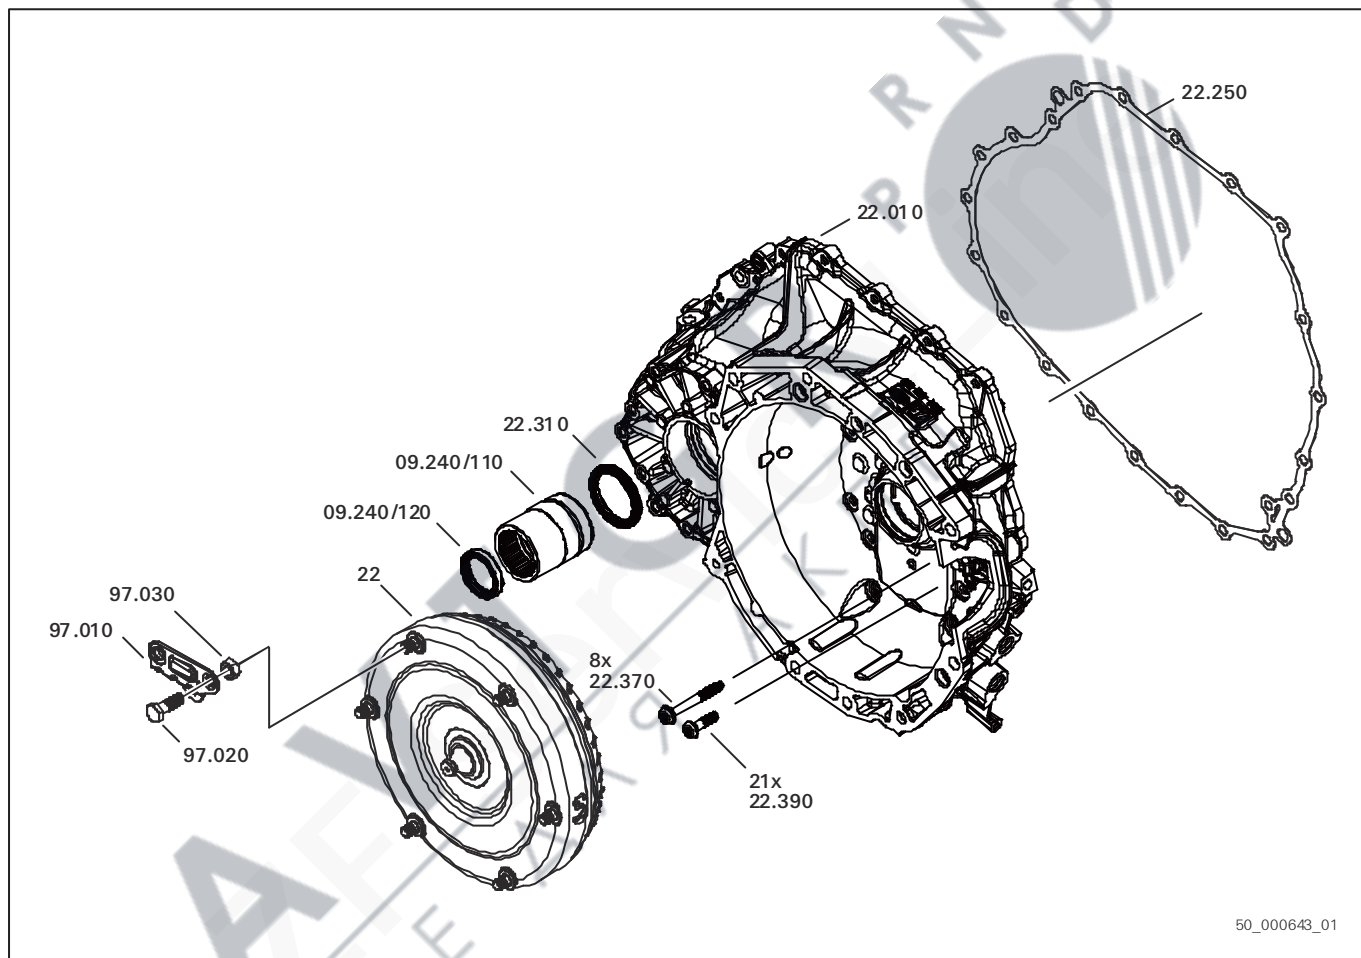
22 - Wandlerglocke, 97 - Wandlerhaltebügel, 09 - Hohlwelle
